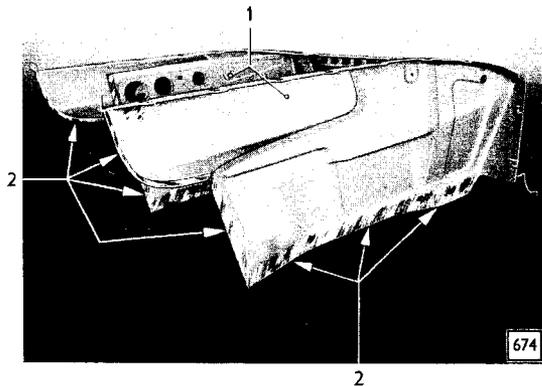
Anlageflächen und Flansche des Zusammenbaues Radeinbauten mit Luftleitblechen blankgesäubert – Ansicht von Radeinbau-Außen-seite
